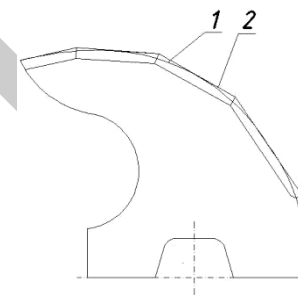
Схема куттерного ножа с ломаной режущей кромкой:
